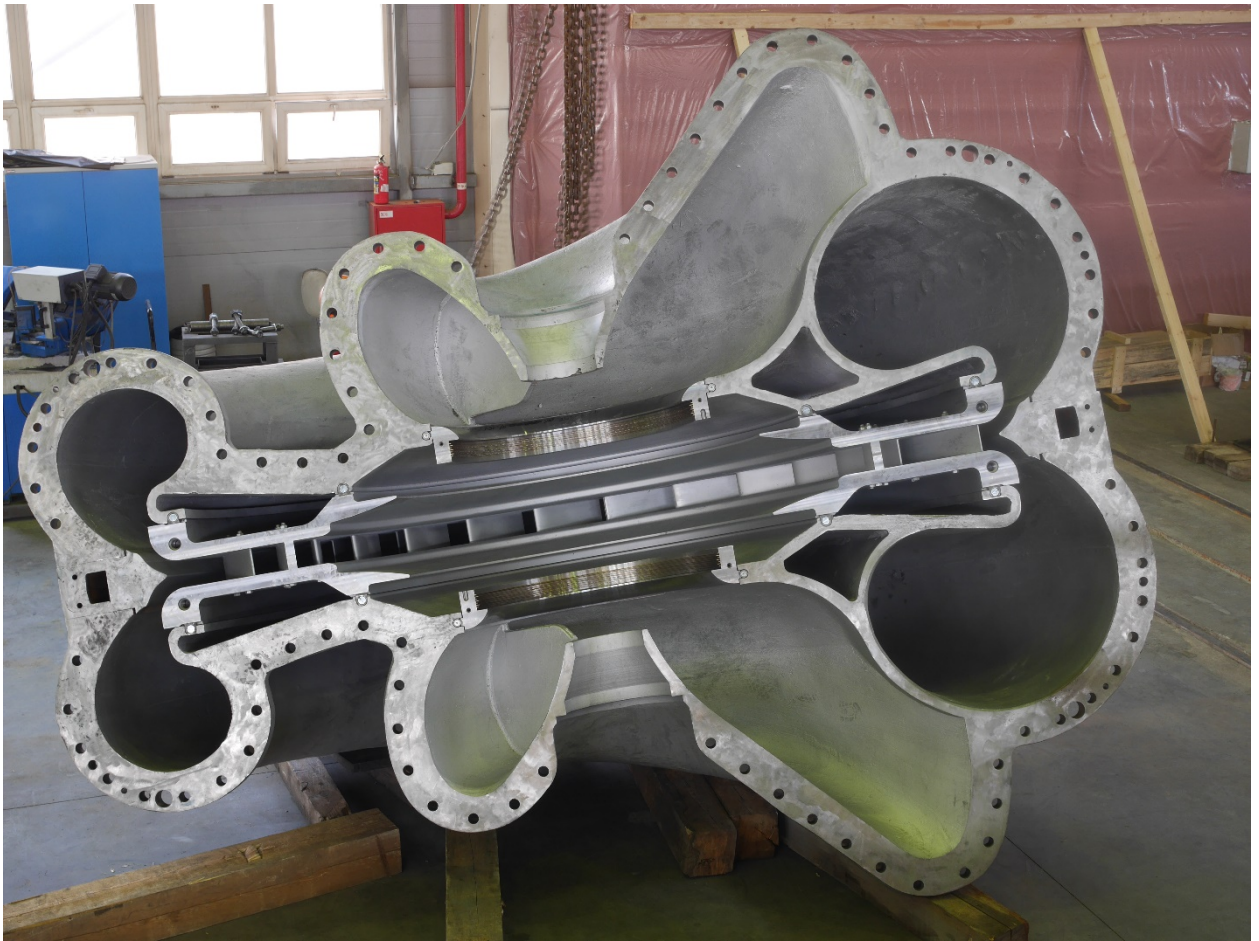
Половина корпуса в сборе с модернизированным диффузором
